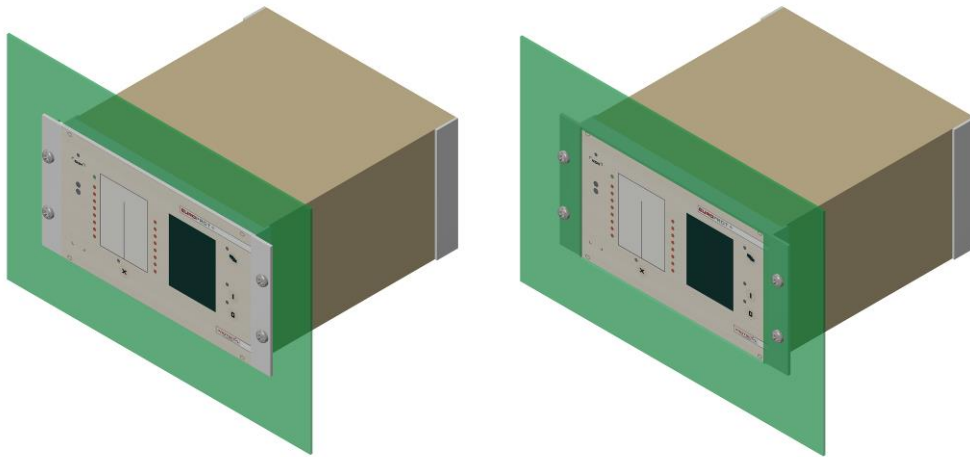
D pour le montage en rack d'un appareil 9" 1/2 (42TE)
